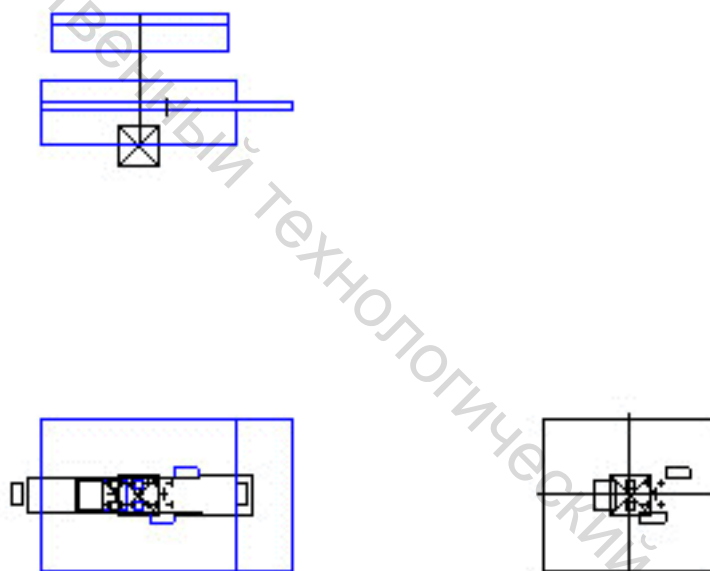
Изображение типового пакета на сборочном чертеже штампа
